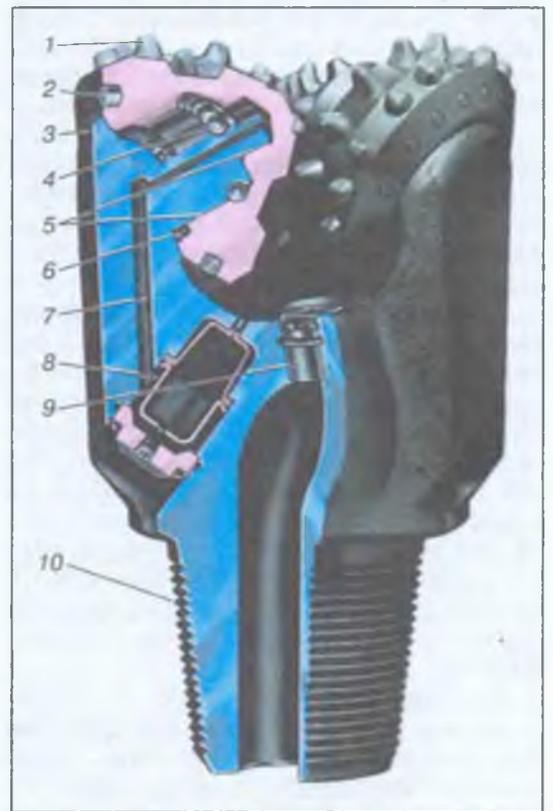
Основные элементы конструкции трехшарошечного бурового гидромониторного долота с твердосплавным вооружением и герметизированными опорами скольжения шарошек: 1 – клиновидные твердосплавные зубья породоразрушающих венцов шарошек; 2 – твердосплавные вставки, упрочняющие обратные конуса шарошек; 3 – козырек лапы; 4 – замковый шариковый подшипник; 5 – основные подшипники скольжения опоры шарошки; 6 – уплотнение полости шарошки; 7 – канал для подачи смазки в подшипники опоры шарошки; 8 – резервуар со смазкой и устройство для компенсации изменения давления при спуске долота в скважину и подачи смазки к подшипникам; 9 – гидромониторная насадка с уплотнением и стопорным кольцом; 10 – замковая резьба для соединения с бурильной колонной.
